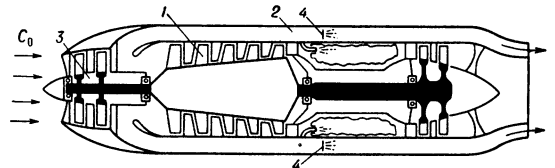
Схема двухконтурного турбореактивного двигателя. 4 — форсунки для дополнительного сжигания топлива во втором контуре.
